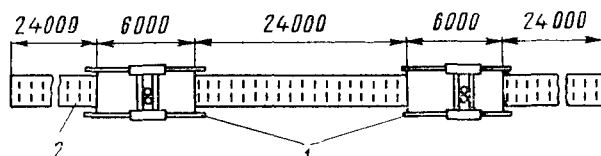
Схема поточной линии контактной сварки боковых стен вагона
